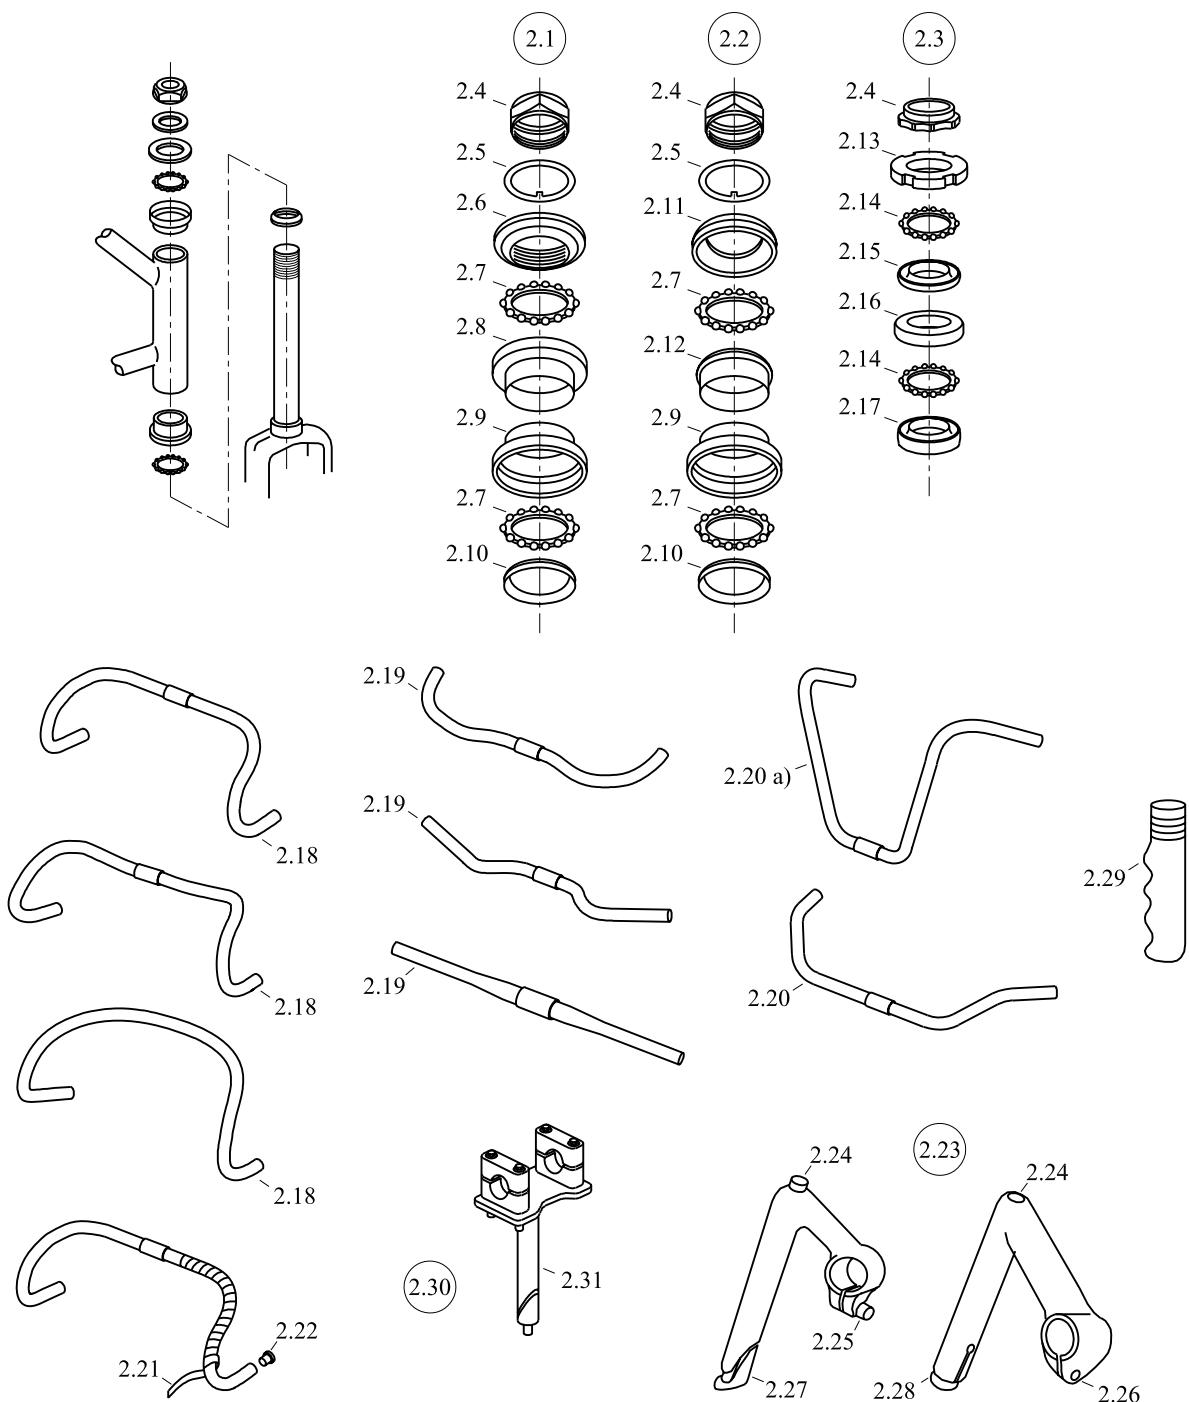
Ensemble de direction / Head assembly / Steuersatz und Lenkung / Gruppo sterzo / Balhoofd samenscholing
